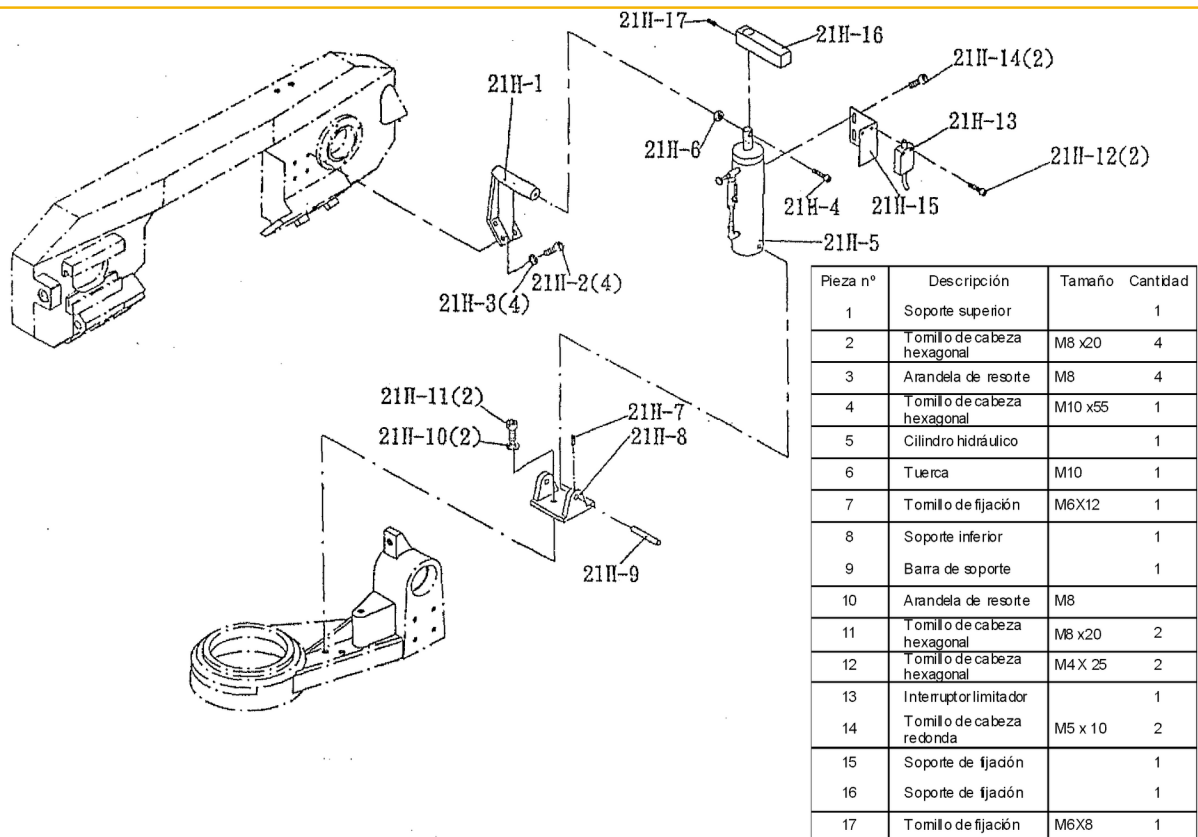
Figure 5 — Bras et groupe hydraulique
